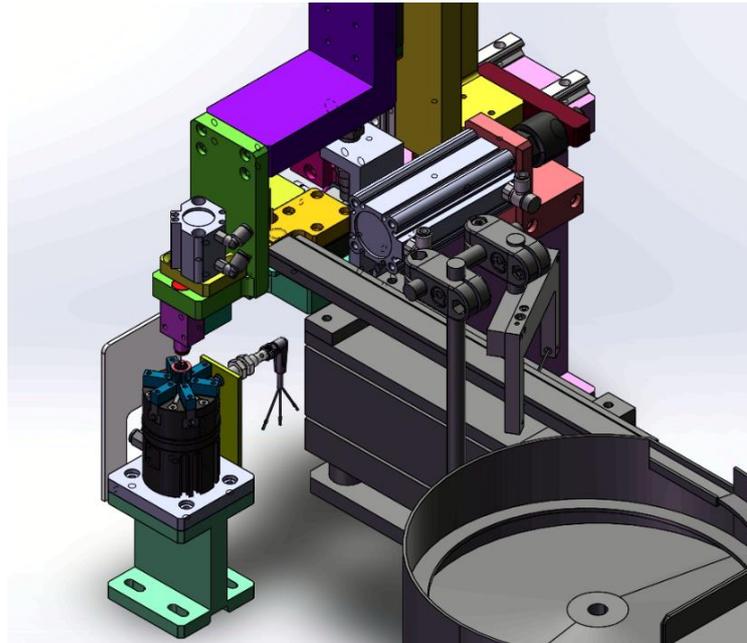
Máquina de separación de junta tórica 4. Fuente:propia
